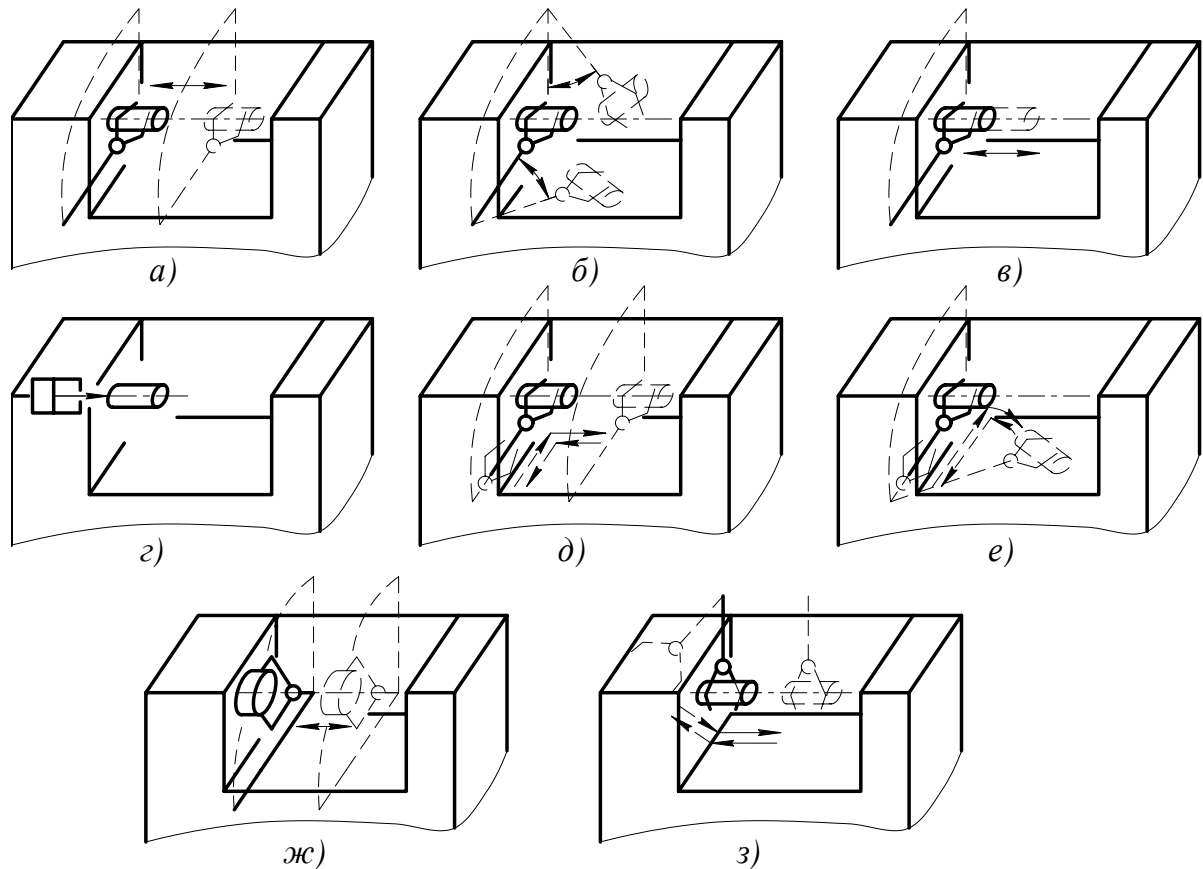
Схеми переміщення деталей на робочу позицію
